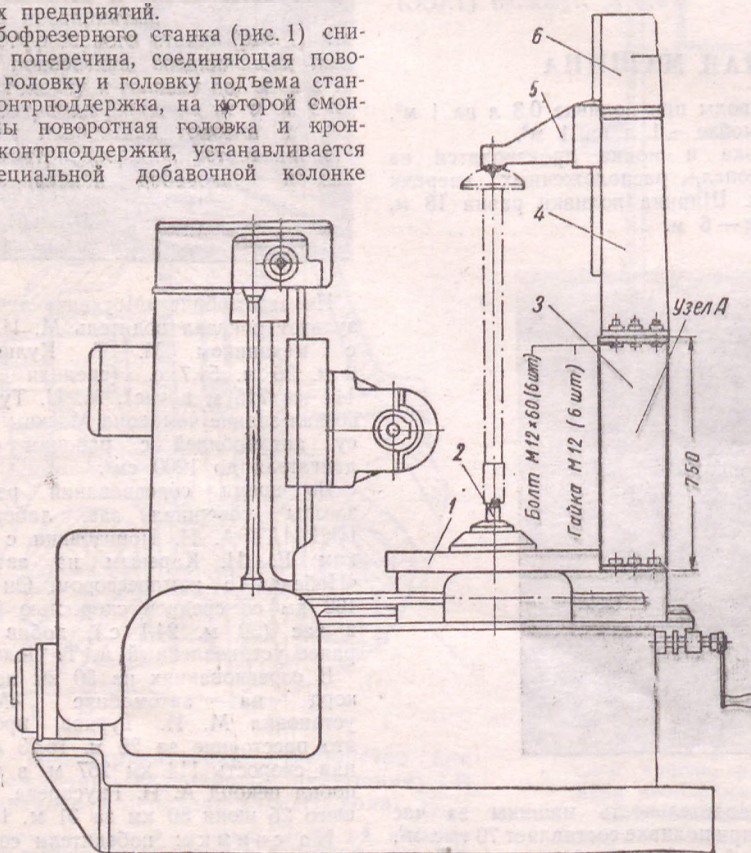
Зубофрезерный станок с добавочной колонкой:
